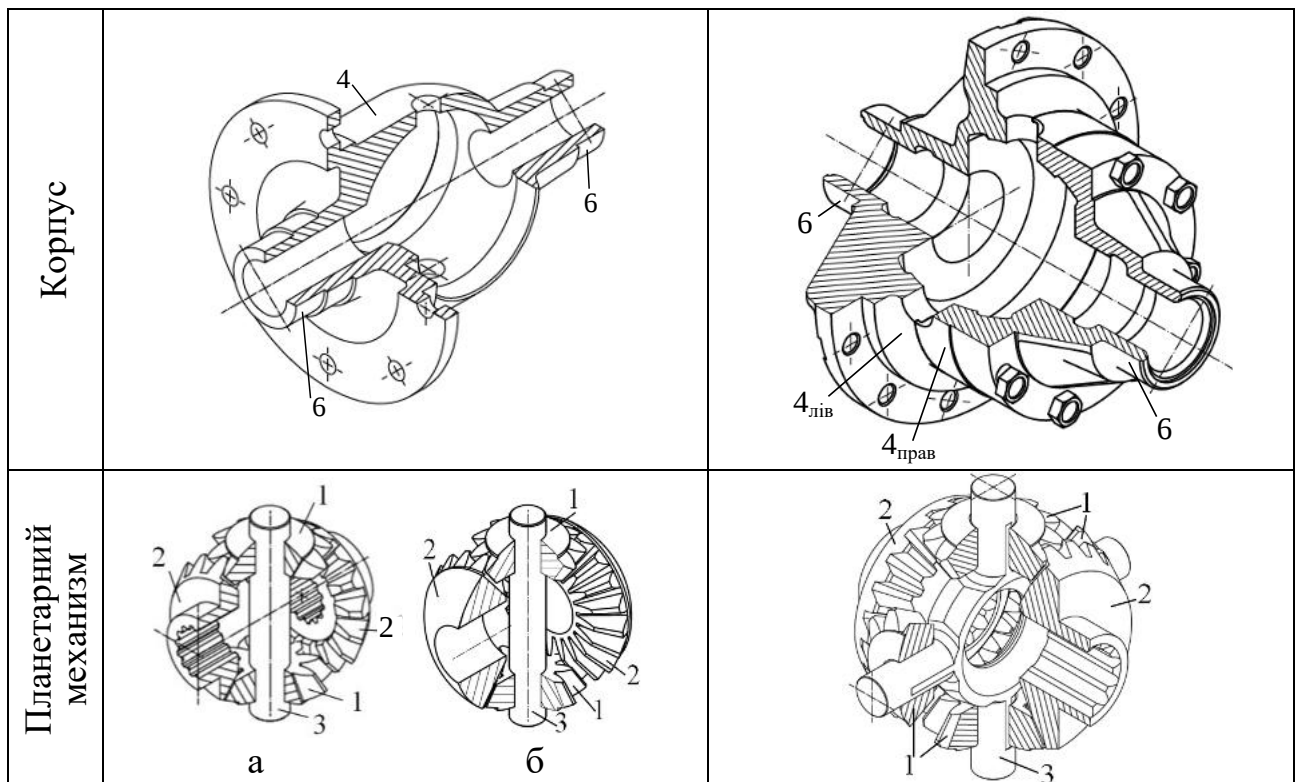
Кінематична схема диференціала з конічним зубчастим зачепленням: 1 – сателіт; 2 – півосьова шестерня; 3 – вісь сателітів; 4 – корпус диференціала; 5 – вісь обертання; 6 – опорні шийки
